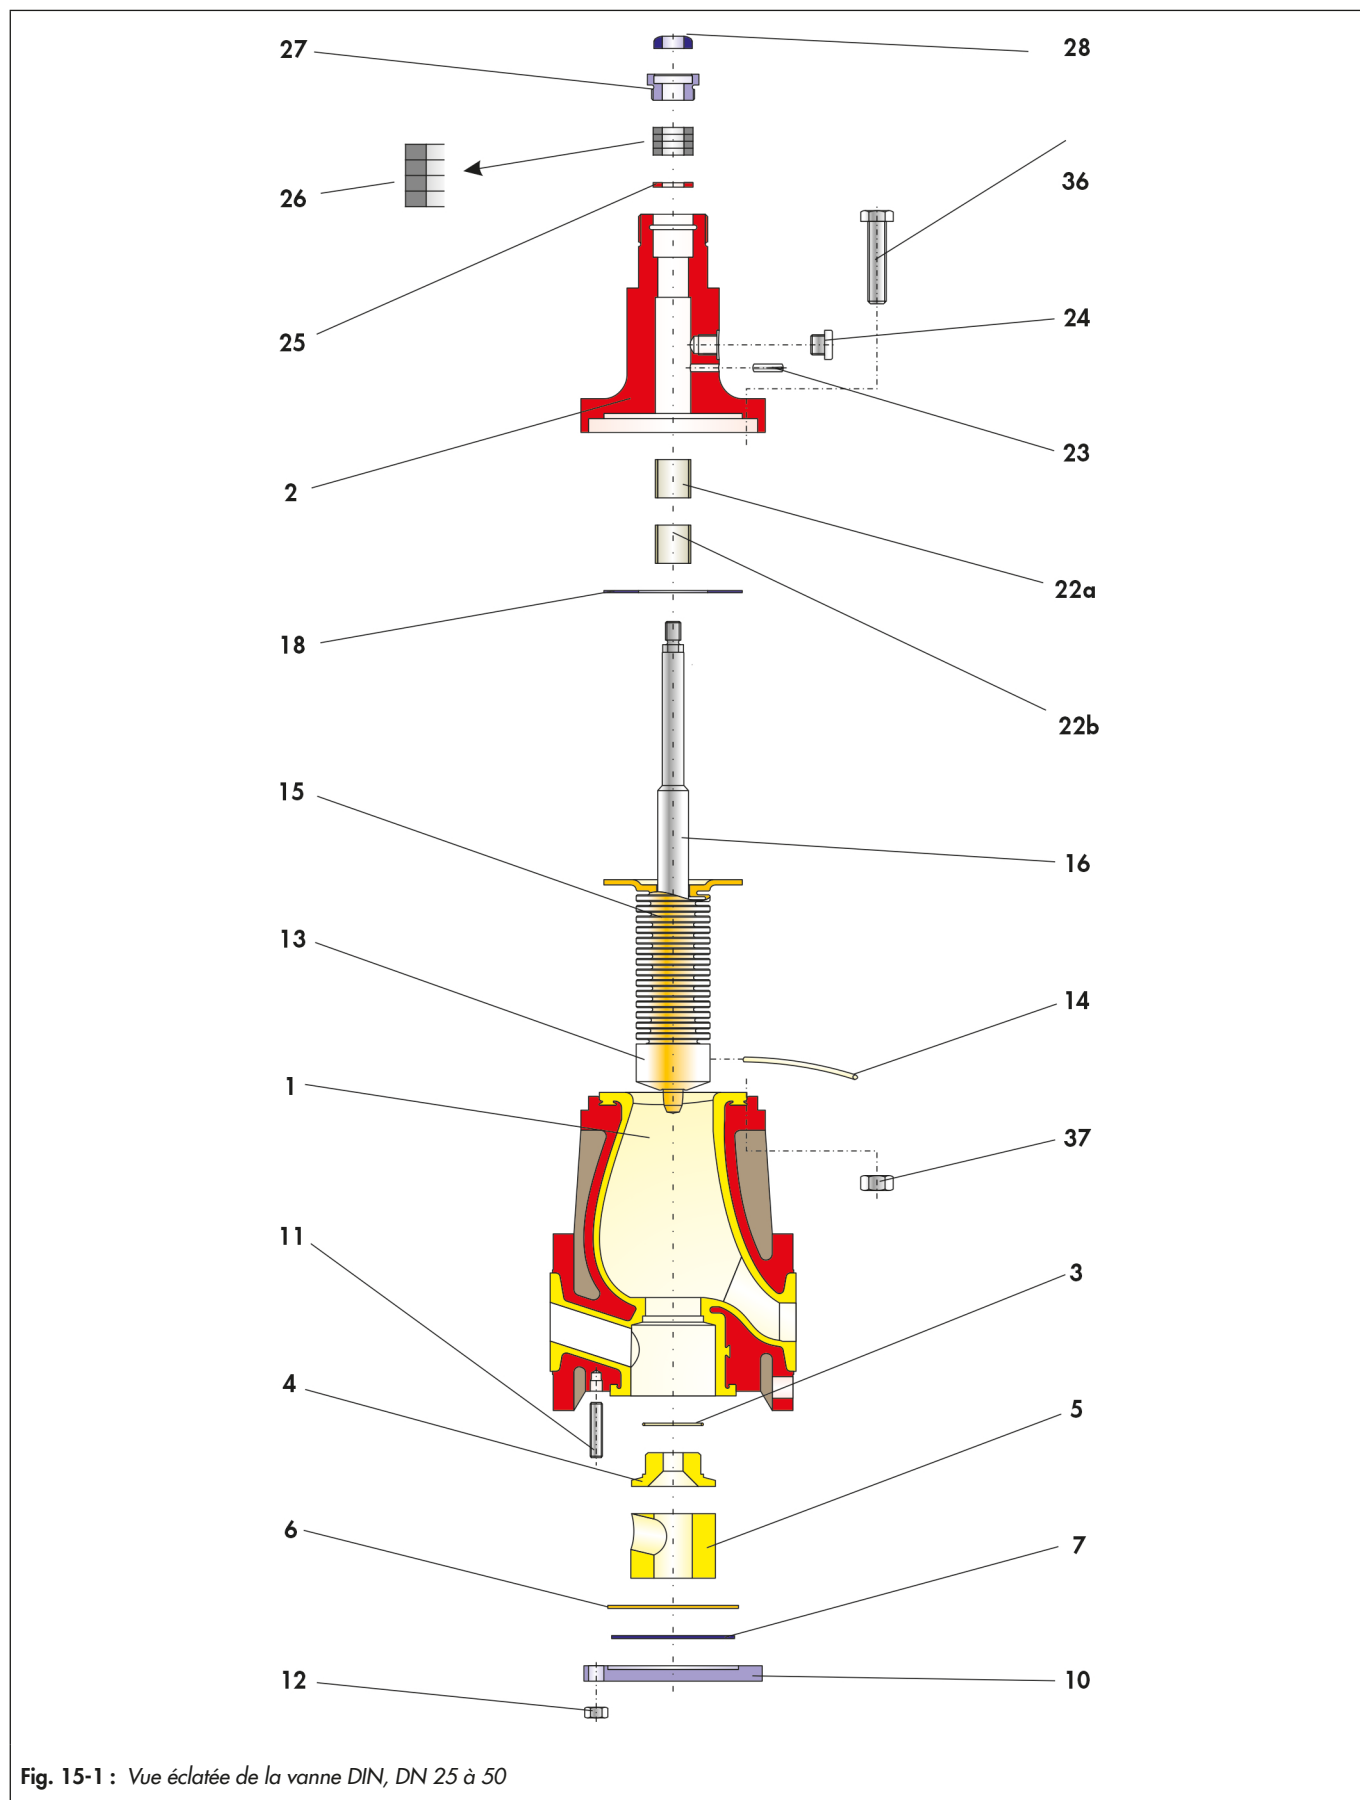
Vue éclatée de la vanne DIN, DN 25 à 50
